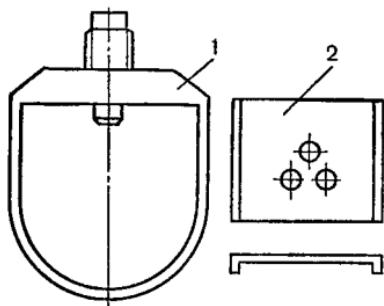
Приспособление для крепления ножа и регулирования захвата косы:
